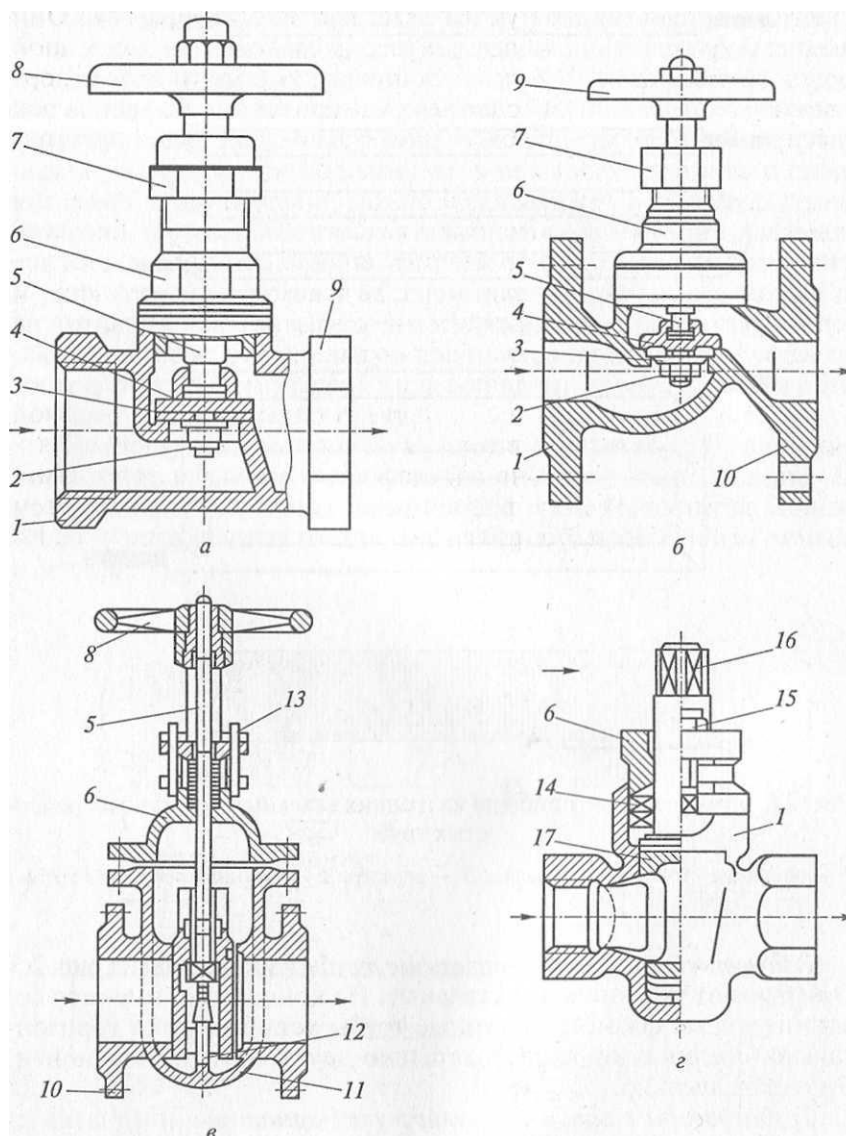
Запорно-регулирующая трубопроводная арматура систем отопления:
